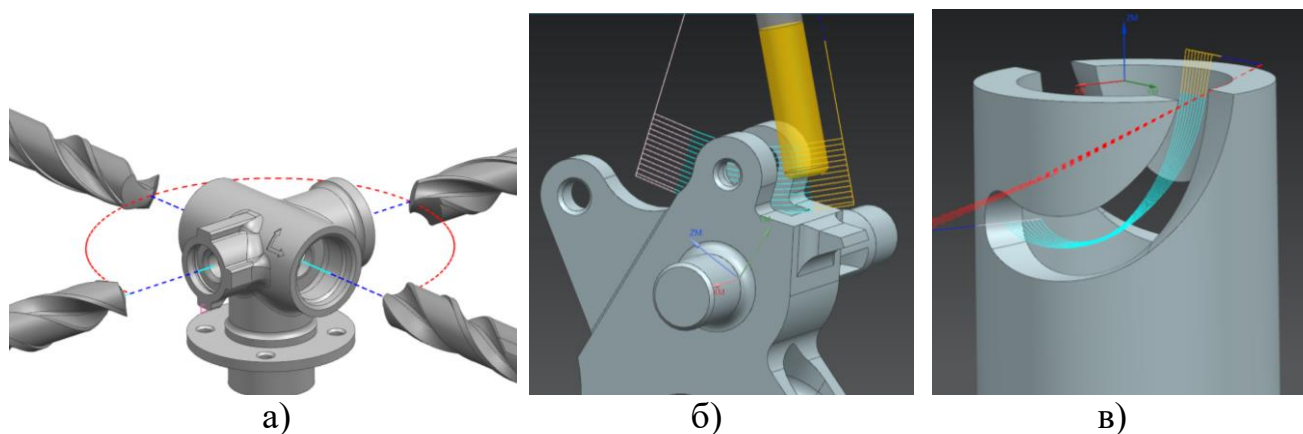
Траектории движения режущего инструмента при пятиосевой обработке: а) позиционное 5-ти координатное сверление, б) непрерывное 4-х координатное фрезерование паза с радиусным дном, в) непрерывное 5-ти координатное фрезерование замковой поверхности
